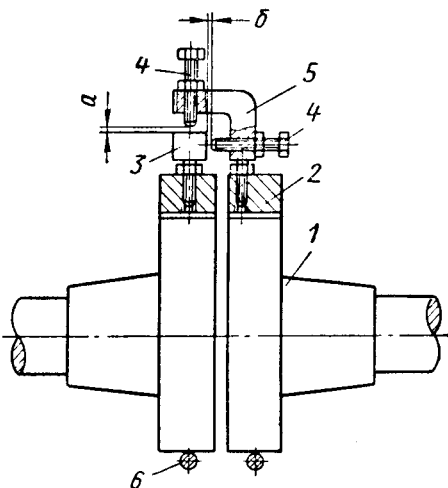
Приспособление для центрирования валов по полумуфтам:
